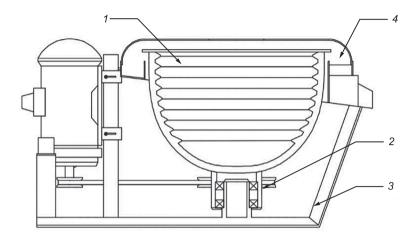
Безнапорный центробежный концентратор. I — рабочий орган в виде чаши; 2 — приводной вал с системой подшипников; 3 — несущая рама; 4 — устройство загрузки и разгрузки продуктов обогащения.
